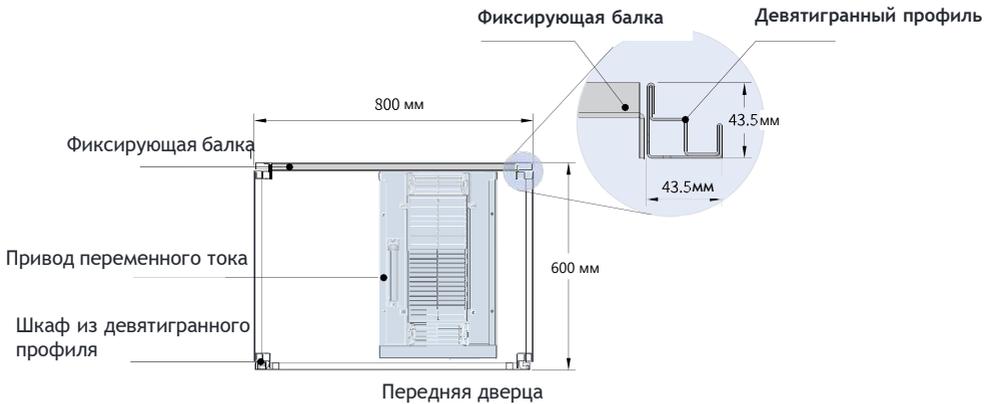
Вид сверху шкафа для моделей T11 и T12
